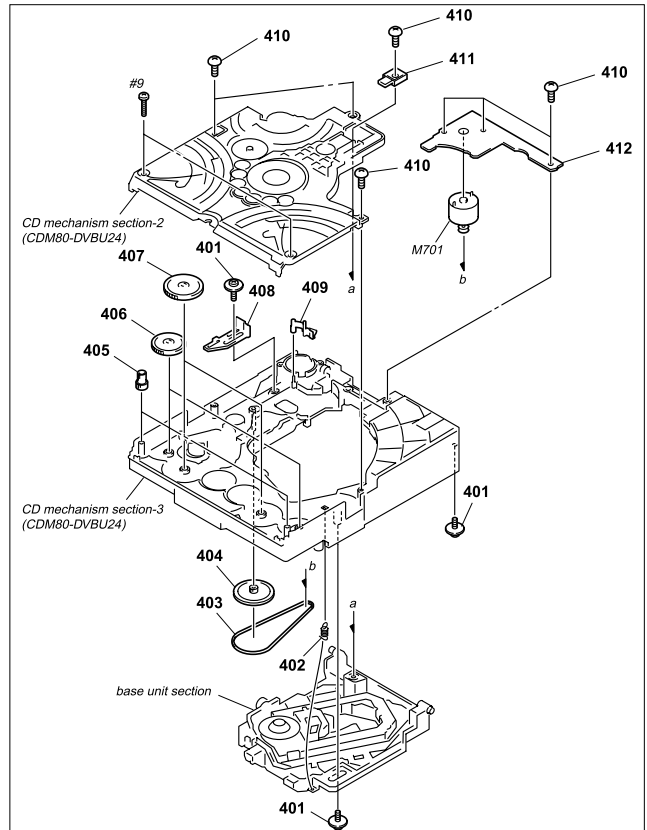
Сборочный чертеж механизма CDM80-DVBU24 (секция 1)
